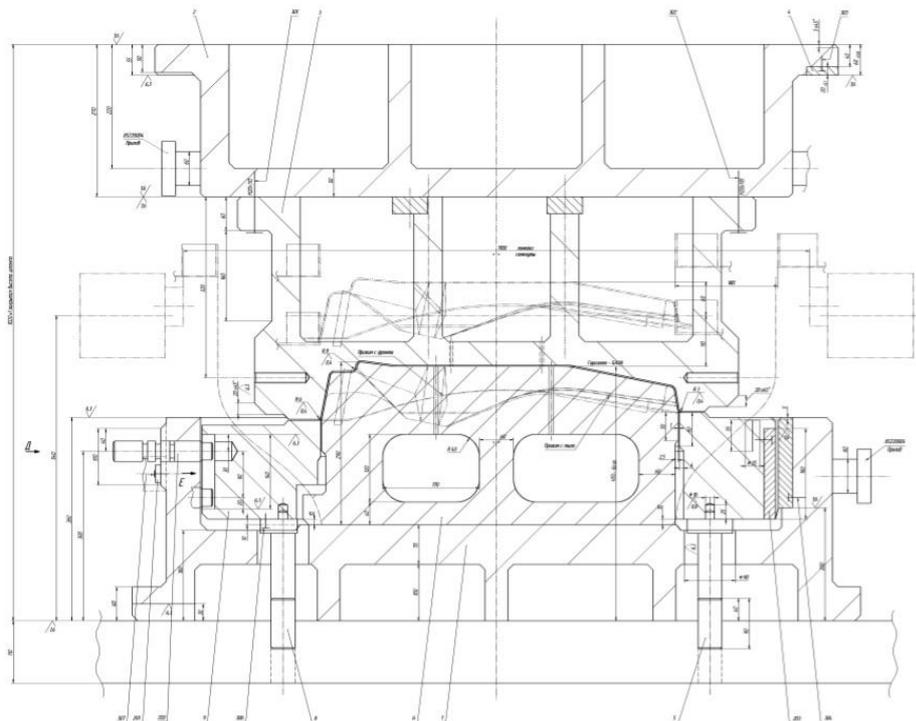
штамп для вытяжки детали «Соединитель лонжерона с полем»
